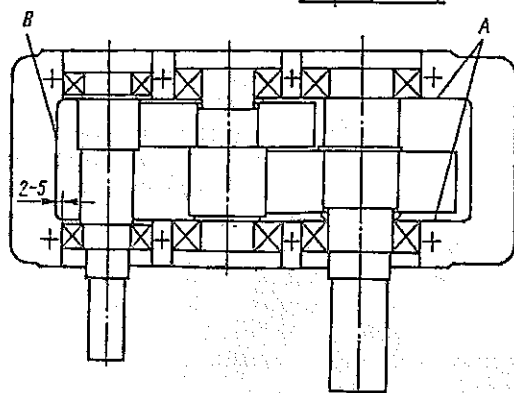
Компоновка двухступенчатого цилиндрического редуктора
